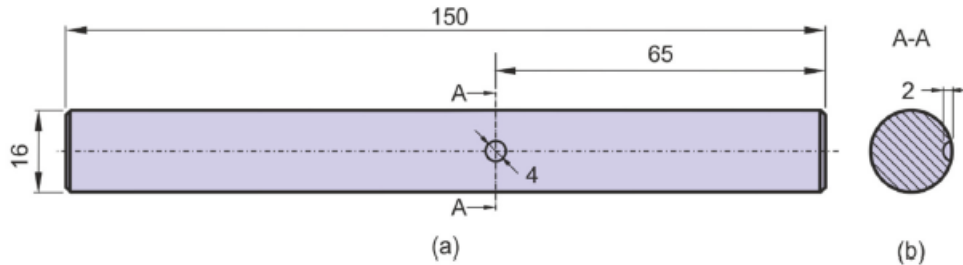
Geometria do provete utilizado: (a) vista frontal; (b) vista transversal (Branco et al., 2019).
